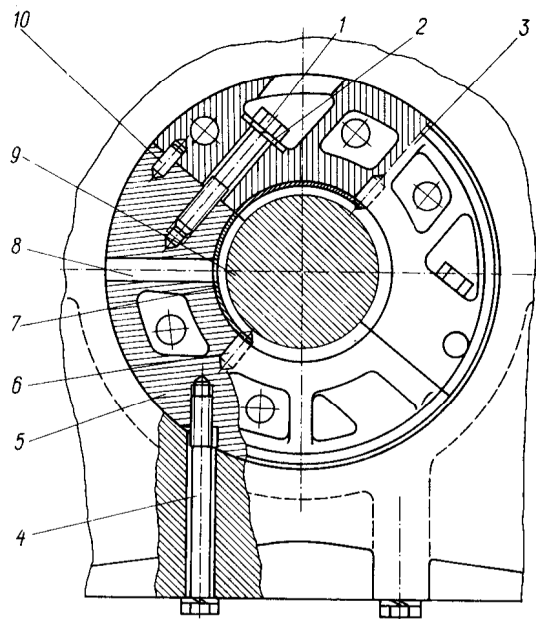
Опора среднего коренного подшипника (вид со стороны носка коленчатого вала):
